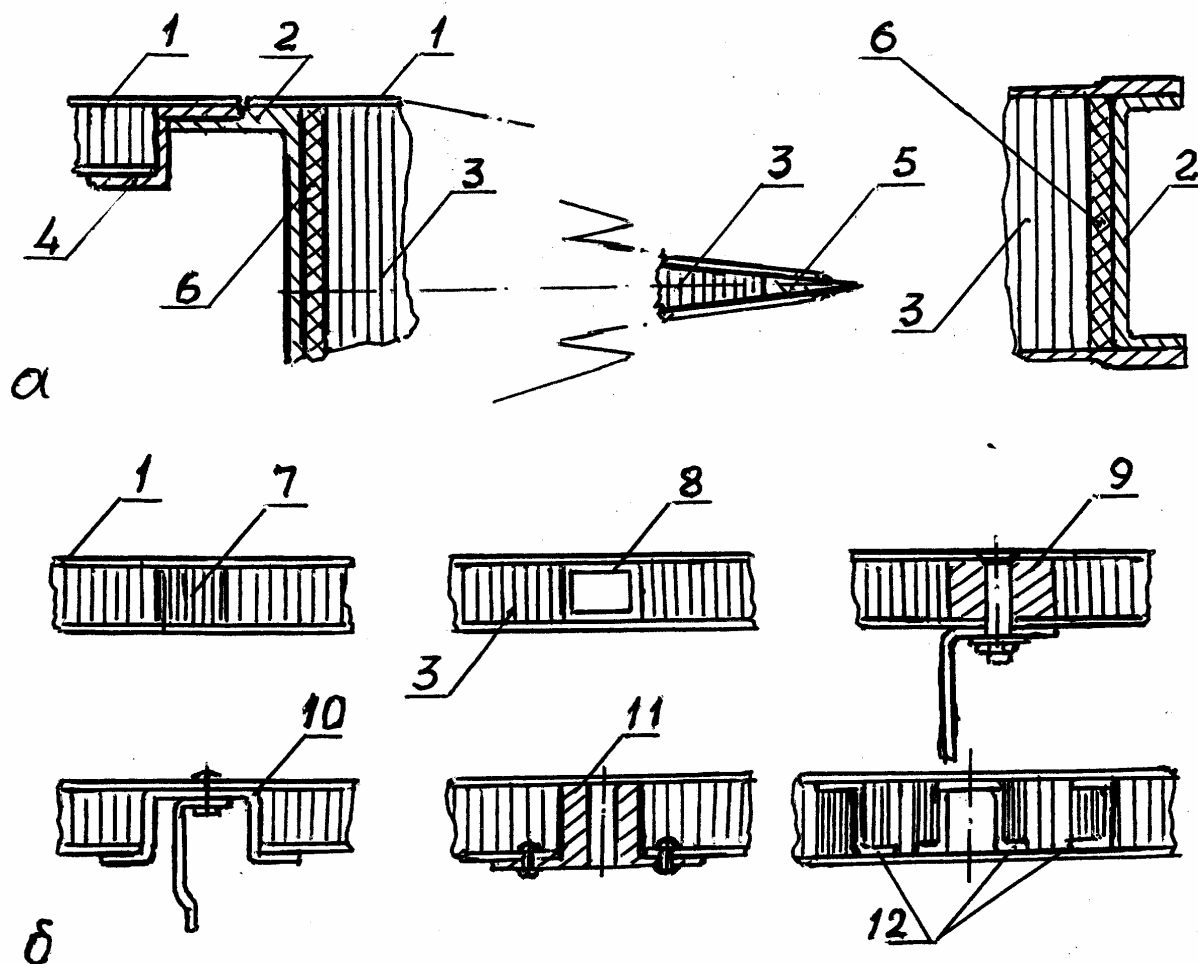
Способы заделки кромок и местного усиления в сотовых конструкциях: а – заделка кромок узлов при использовании ПКМ; б – участки узлов сотовых конструкций, воспринимающих сосредоточенные нагрузки. 1 – обшивка; 2 – стыковочный профиль (лонжерон, стенка); 3 – сотовый наполнитель; 4 – стыковочный профиль панели; 5 – законцовочный профиль; 6 – вспенивающаяся композиция; 7 – уплотненный сотовый наполнитель; 8 – усиливающий профиль прямоугольного сечения; 9, 11 – вклеенные втулки разной конструкции; 10, 12 – усиливающие профили
